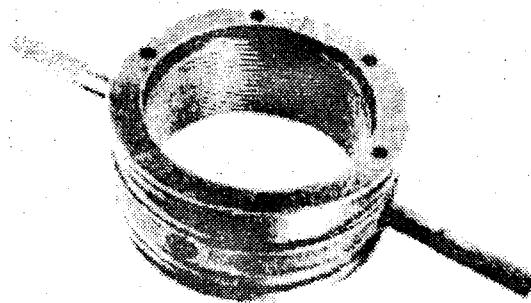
Кольцевой калибр трапециевидной резьбы
